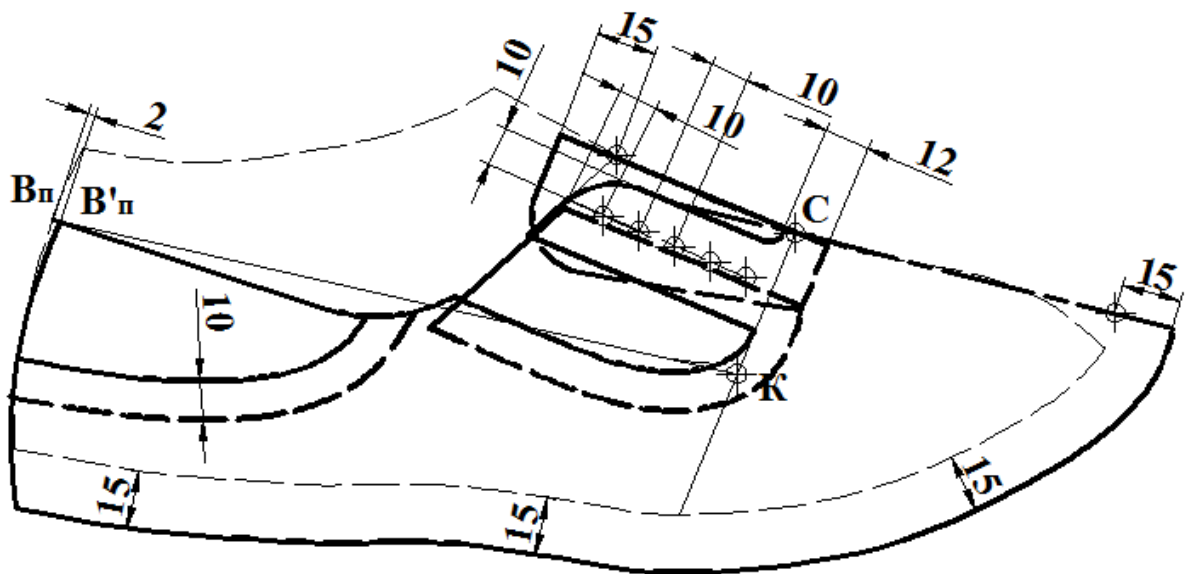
Побудова ґрунд-моделі макету заготовки
